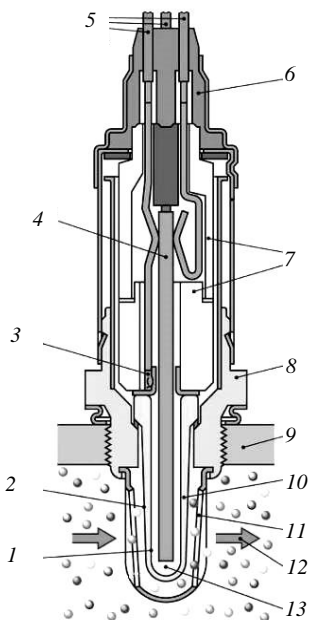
Устройство датчика остаточного кислорода: 1 – положительный электрод; 2 – отрицательный электрод; 3 – контактные площадки; 4 – нагревательный элемент; 5 – контакты датчика и нагревательного элемента; 6 – изолятор; 7 – керамические трубки; 8 – корпус; 9 – выпускной трубопровод; 10 – керамический наконечник; 11 – защитный колпачок; 12 – отработанные газы; 13 – эталонный воздух
